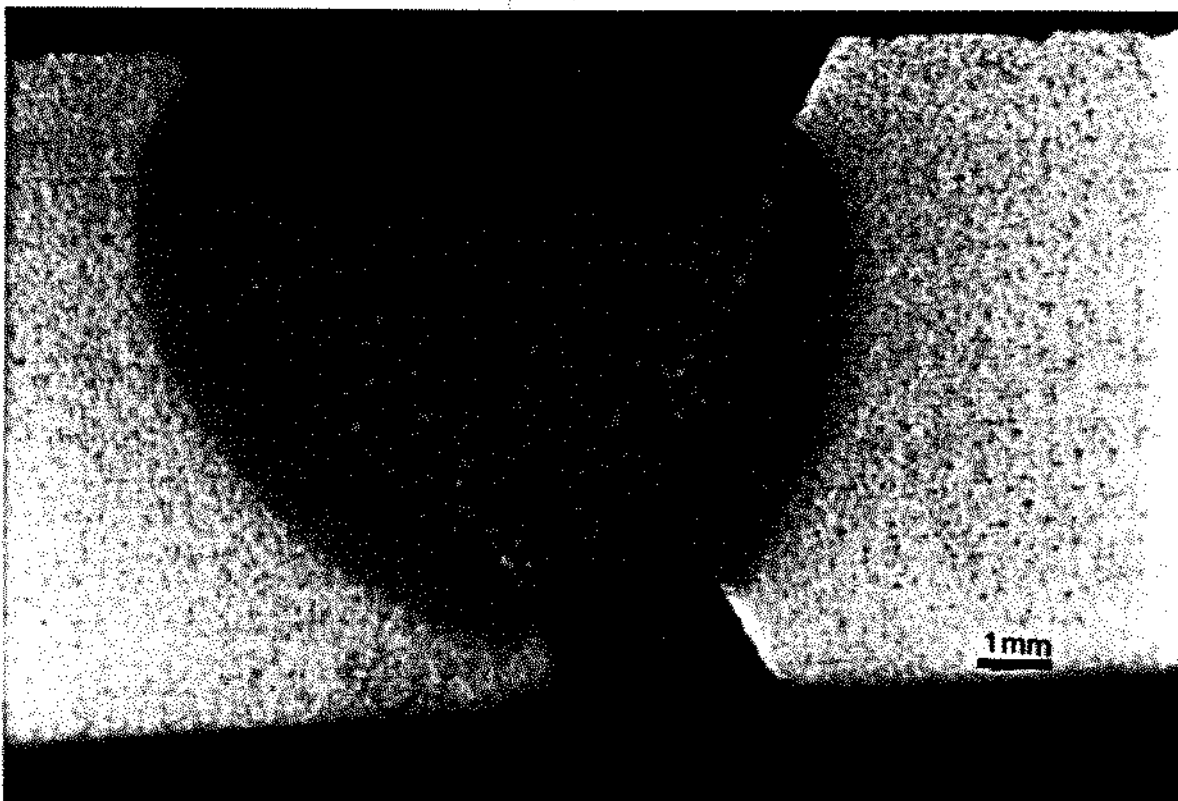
c -Trinca de Seção na ZAC e no Metal de Solda (ZAC/MS)
